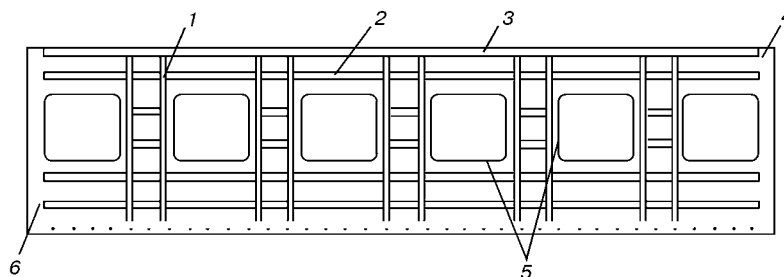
Схема модуля боковой стенки: 1 — стойка; 2 — балка; 3 — верхняя балка; 4 — верхний ряд обшивки; 5 — оконный ряд обшивки; 6 — нижний ряд обшивки
